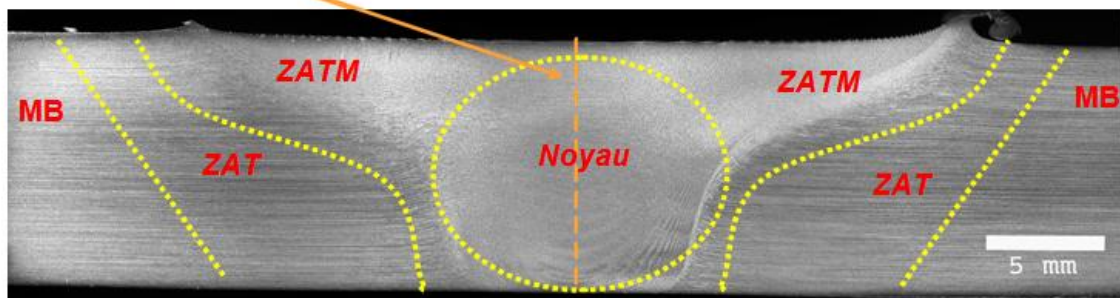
Macrographie d'une soudure FSW d'un alliage d'aluminium [51].
